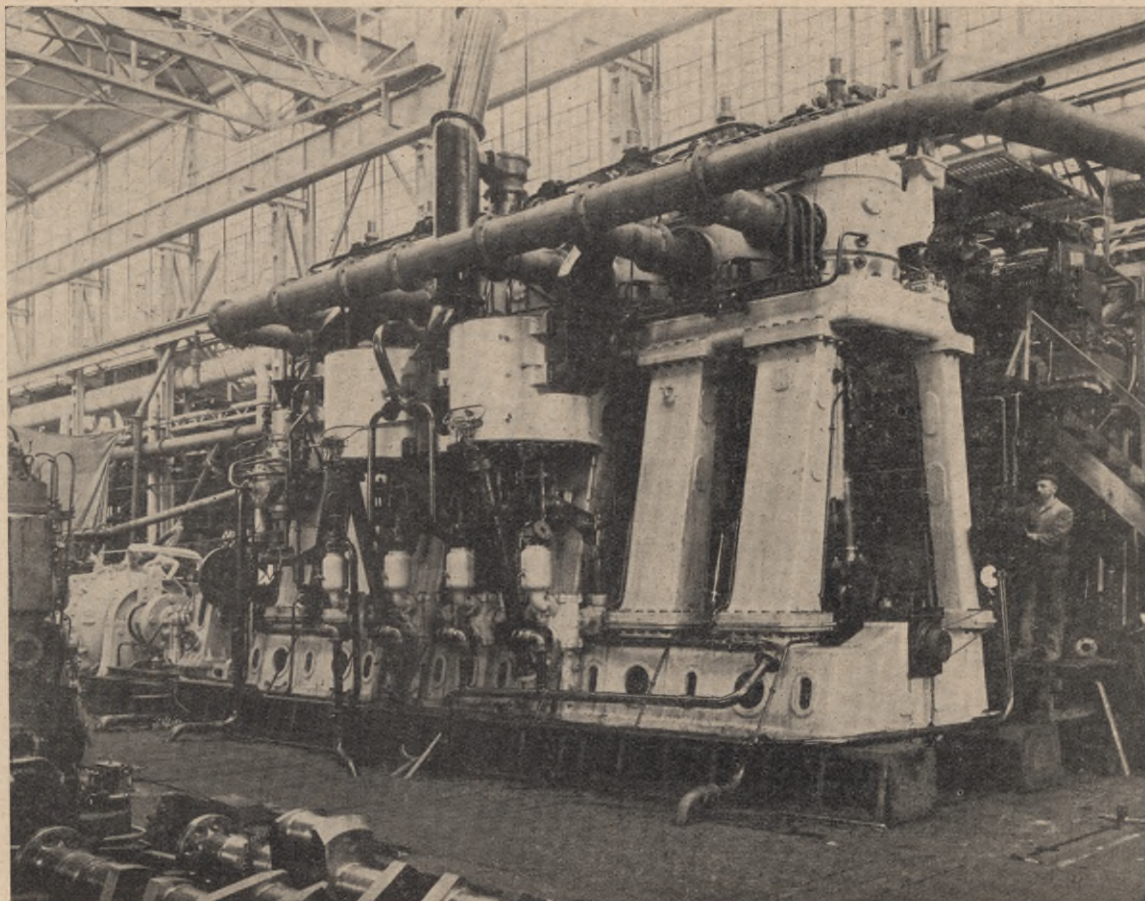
Hinteransicht eines Dieselmotors der „Loki“
